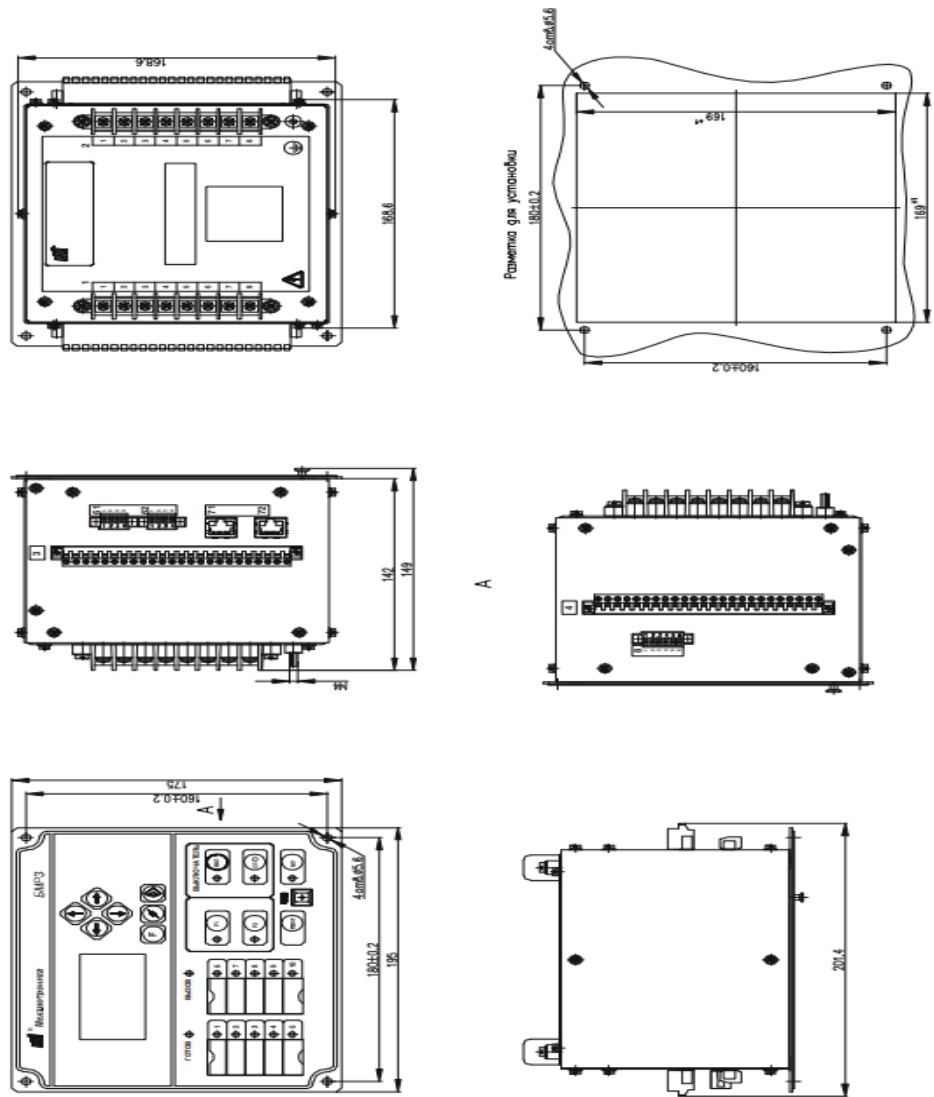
Габаритные и установочные размеры терминала БМРЗ
